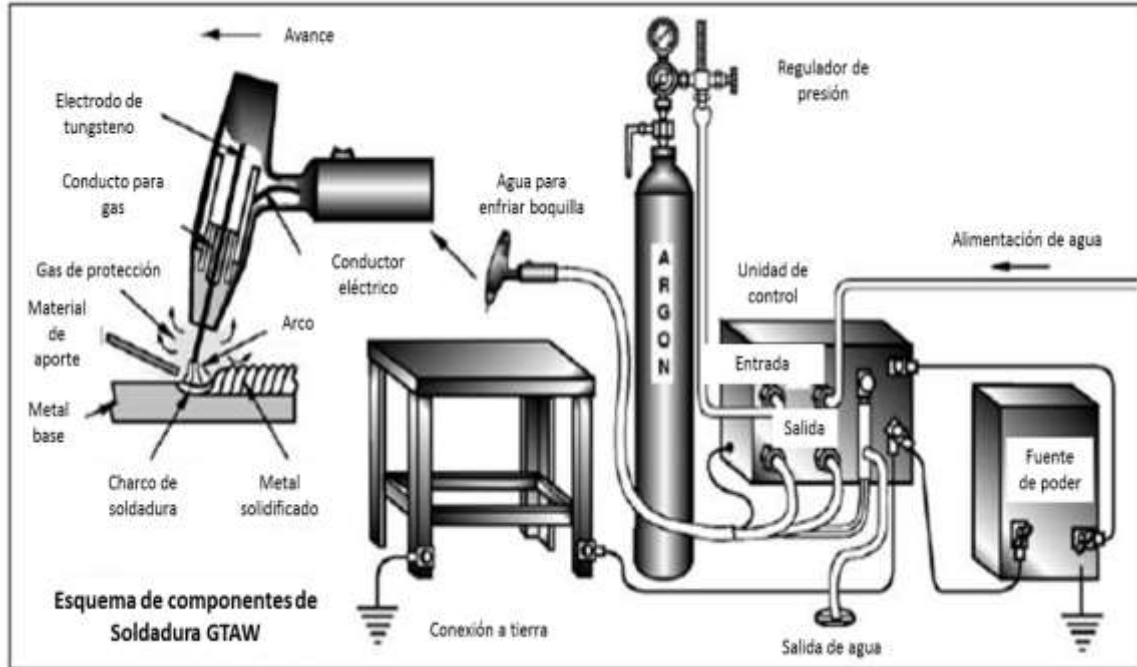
4 Esquema de principales componentes de soldadura GTAW (2)
